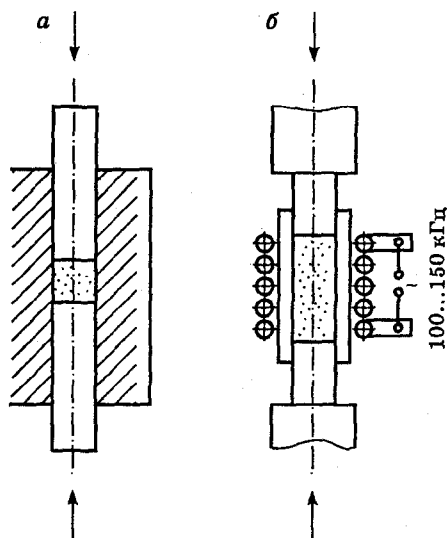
Схема двустороннего прессования порошковых материалов: а — без нагрева; б — с нагревом
